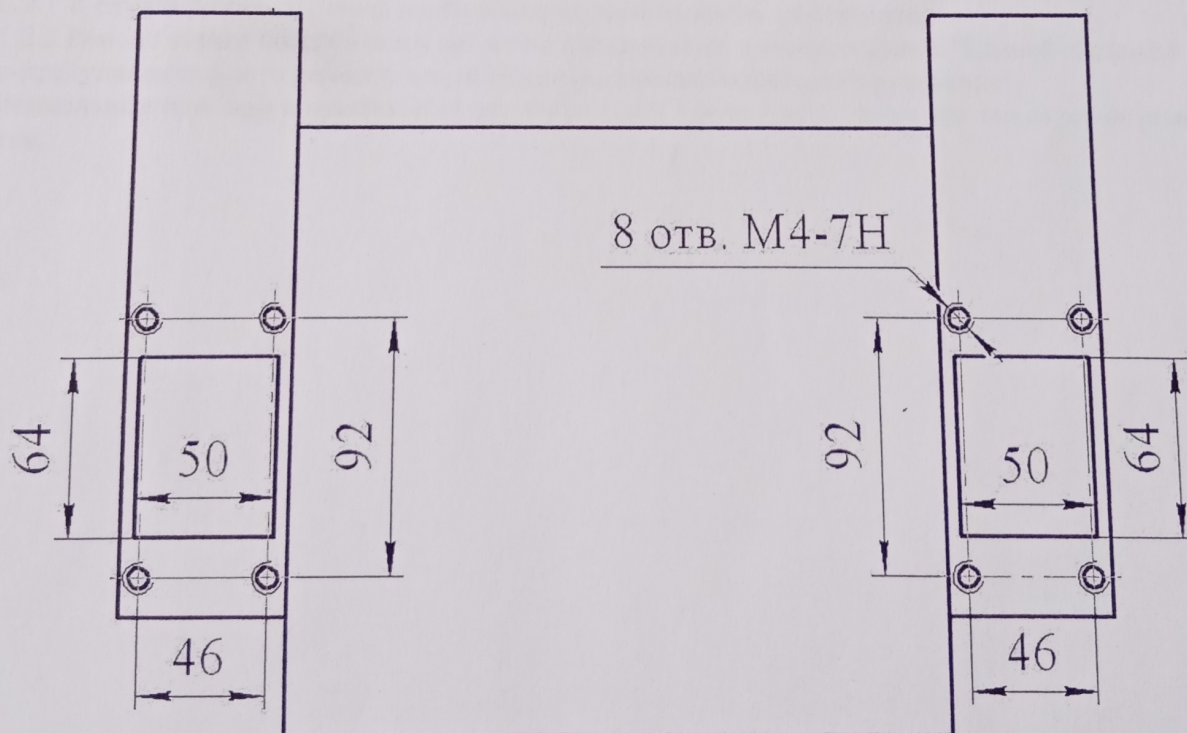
Места для крепления патрубка для подключения пылеотсасывающего агрегата.
